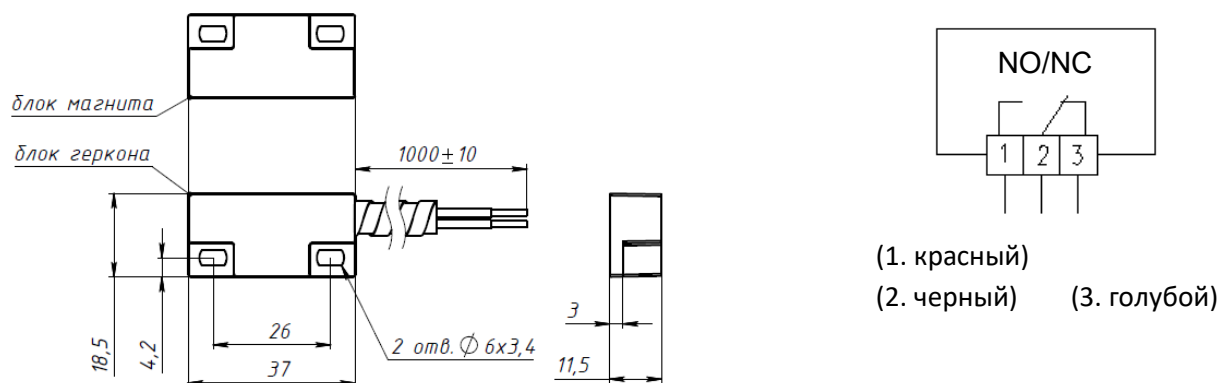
габаритные и присоединительные размеры датчика ДПГ с корпусным магнитом
